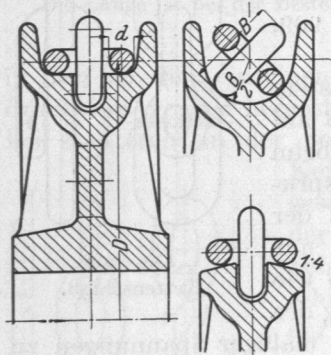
bis 912. Rillenformen an Kettenrollen.
